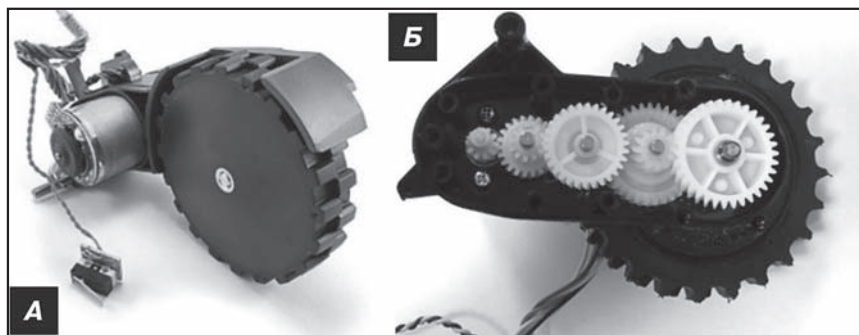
Мотор-редуктор: а — электродвигатель и редуктор в сборе; б — редуктор со вскрытым корпусом
